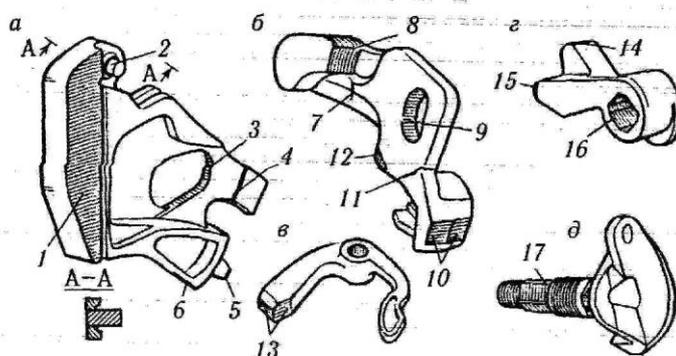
Износы и повреждения деталей механизма сцепления автосцепок
